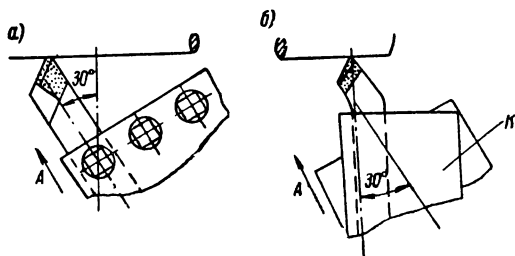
Нарезание резьбы при подаче резца под углом к оси детали, равным половине угла профиля резьбы.
